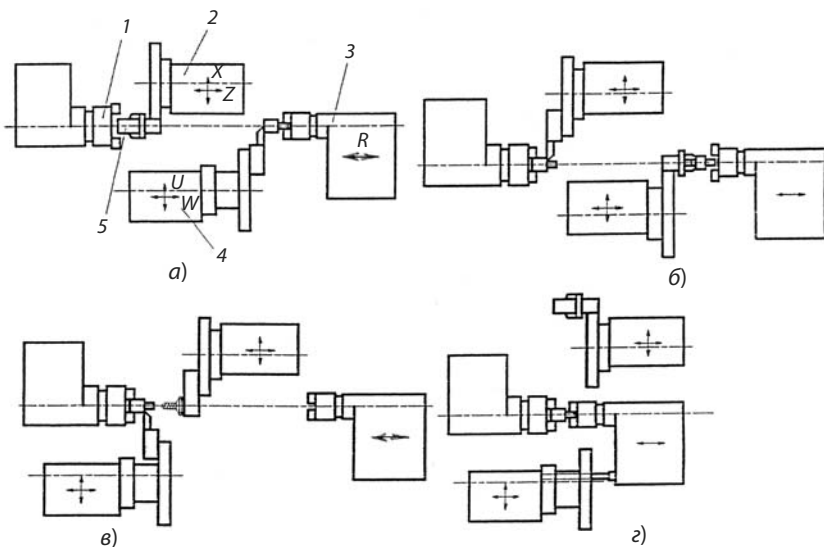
Последовательность обработки заготовки на станке с двумя револьверными головками и протившпинделем:
